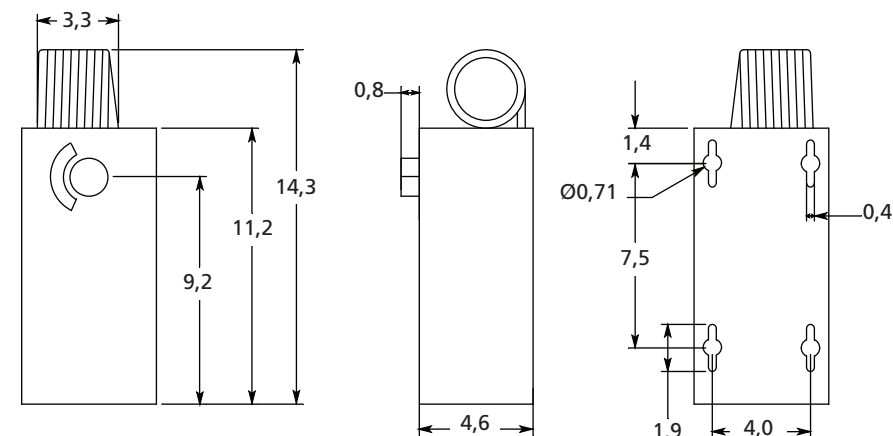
Dimensions du thermostat avec boîtier en métal (en cm)
